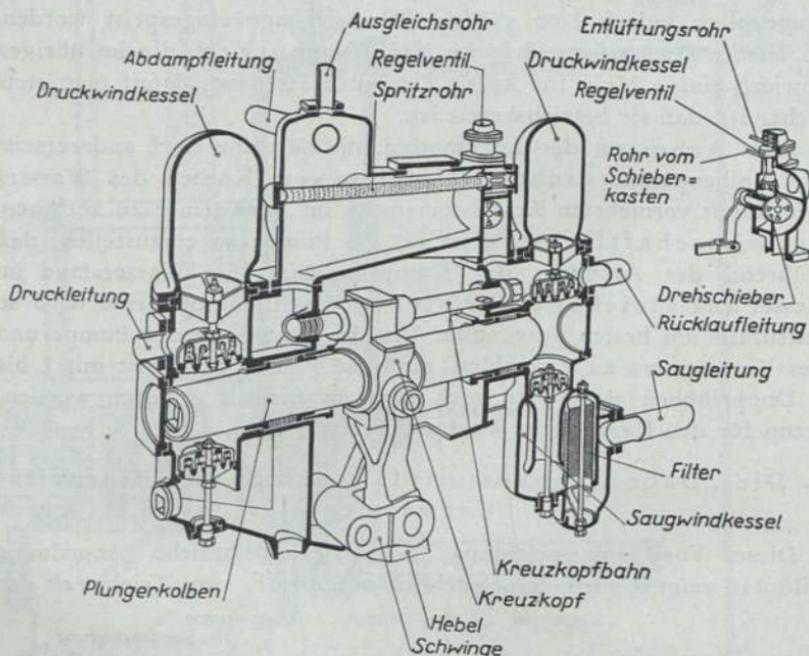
„Dabeg“-Lokomotivfahrpumpe mit Einspritzvorwärmer
